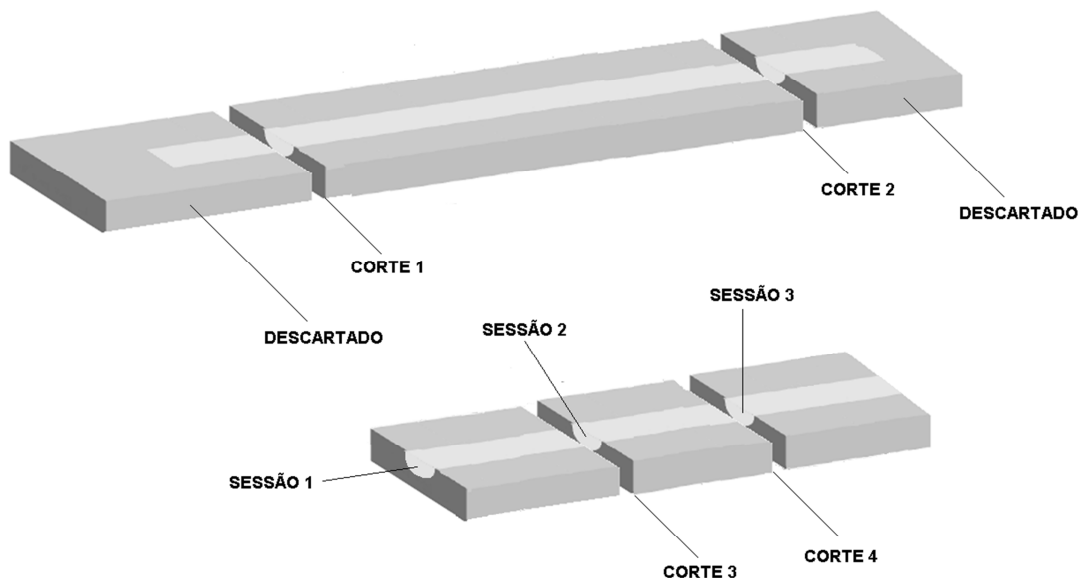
Cortes do corpo de prova para realização da medição da geometria da soldagem
